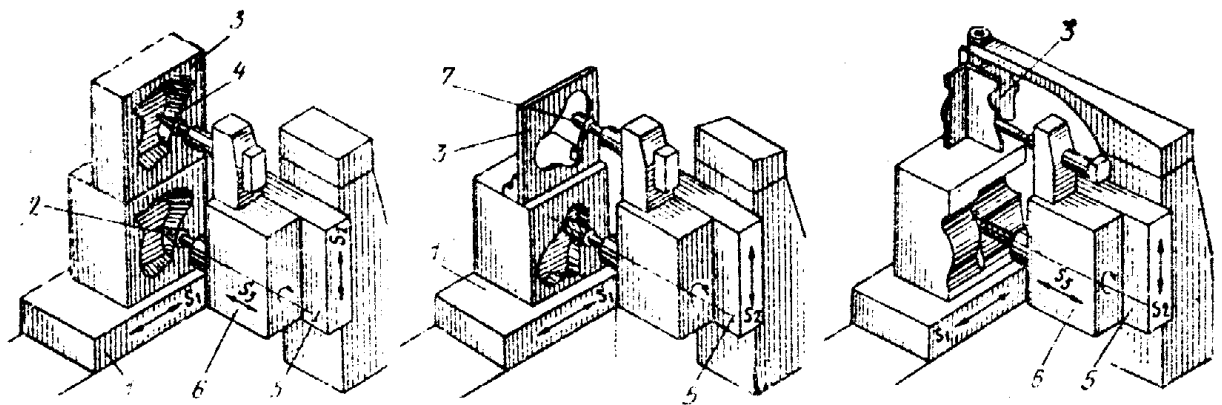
Схемы фрезерования при поступательном перемещении копира и детали
